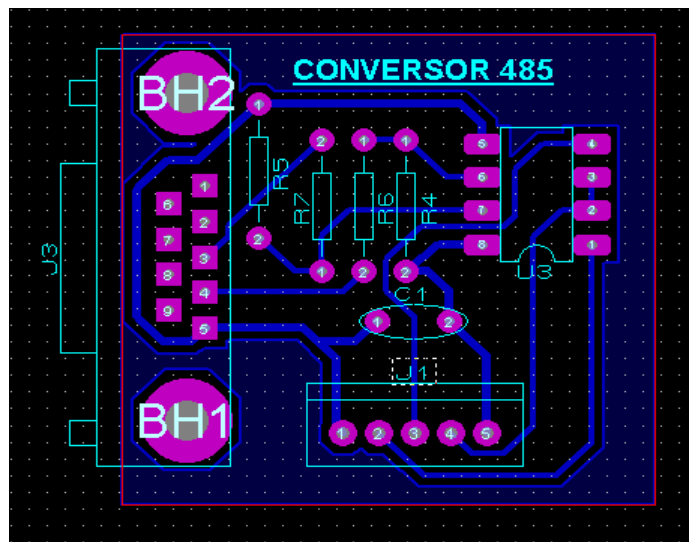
Diseño de la placa de conversor RS232 a RS485
